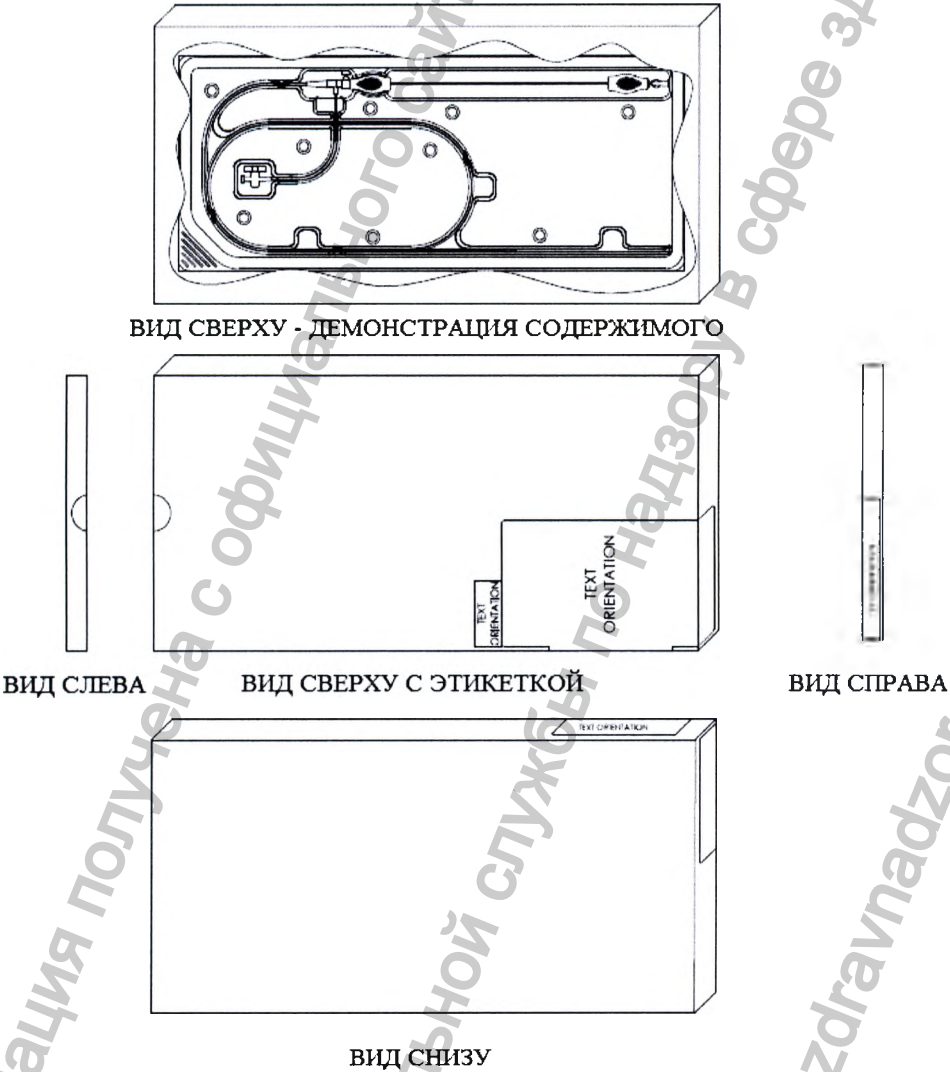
Чертеж вторичной упаковки (общий вид)
